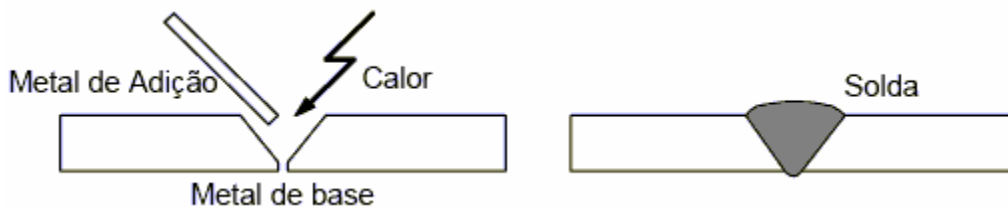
Soldagem por fusão com metal de adição (MODENESI e MARQUES, 2000)
